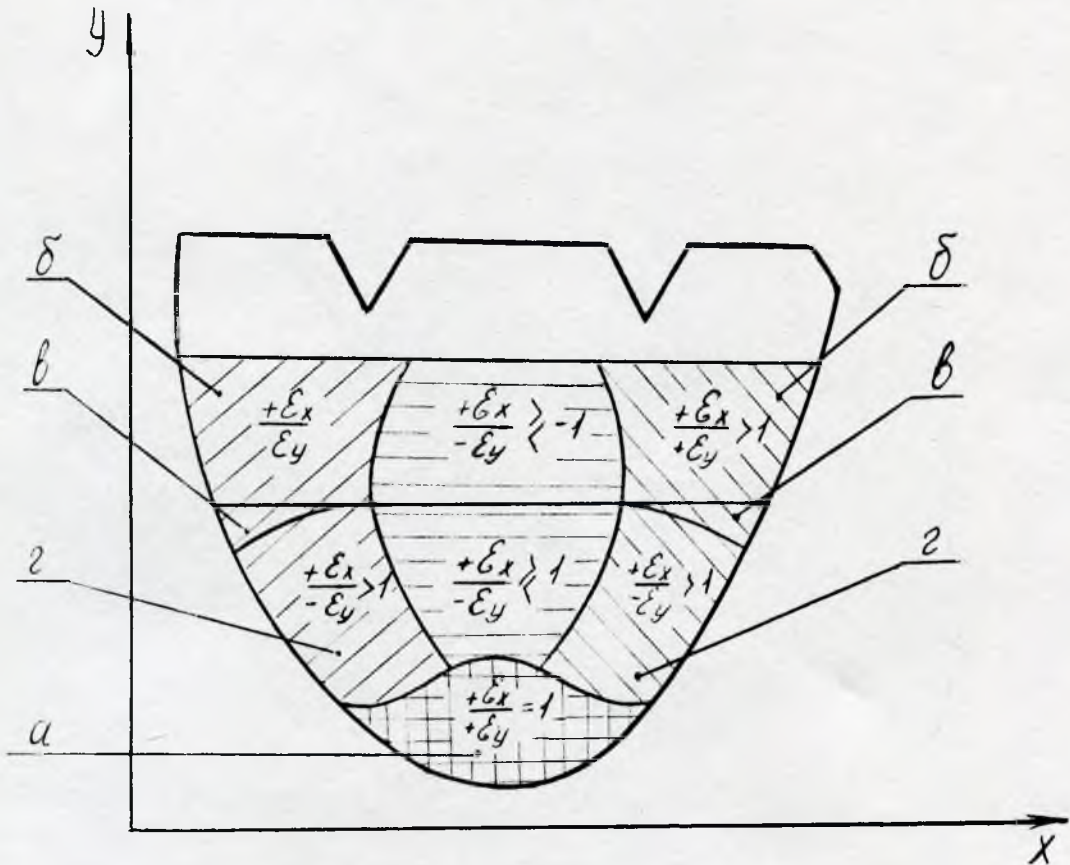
Деформация заготовки при формовании на машинах типа ЗНК.
